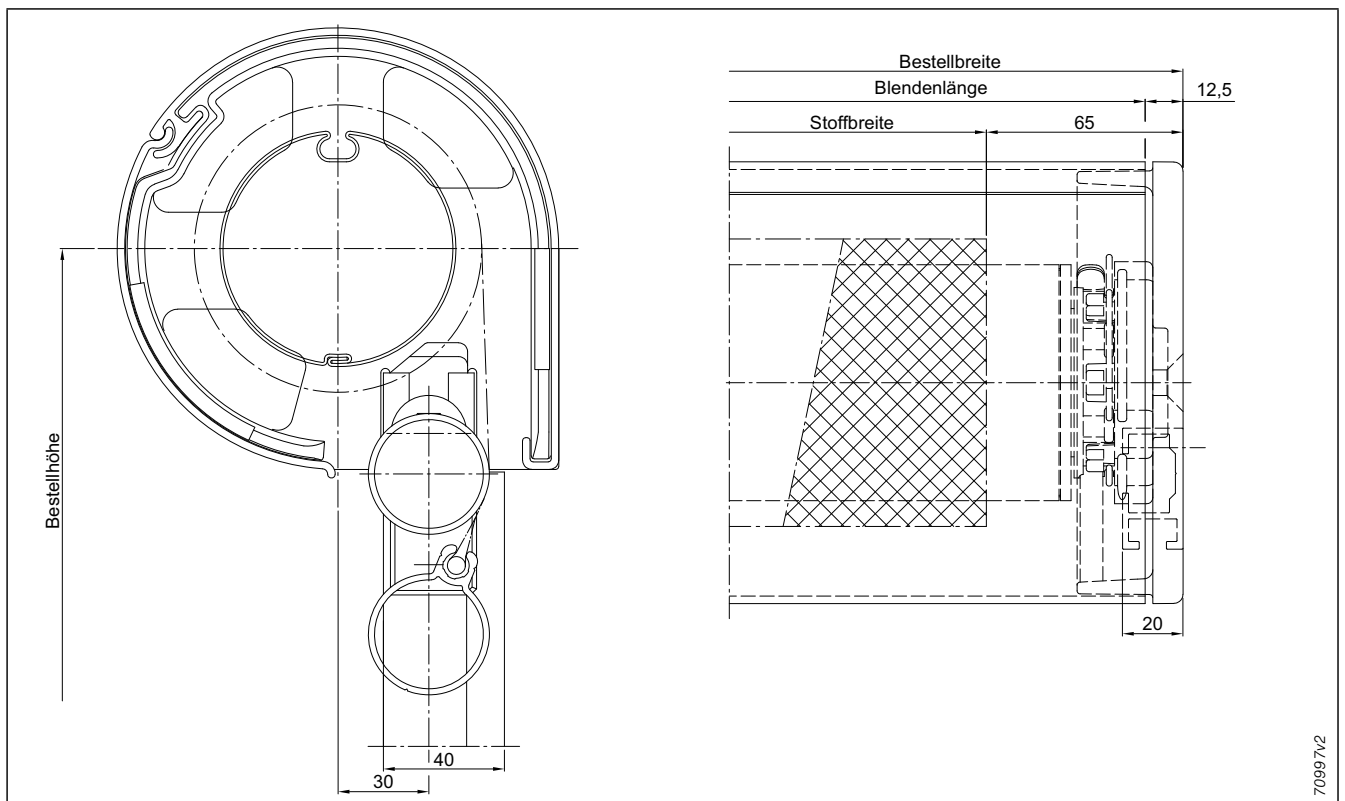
Markisolette 101, mit Rundblende Typ 8.3
